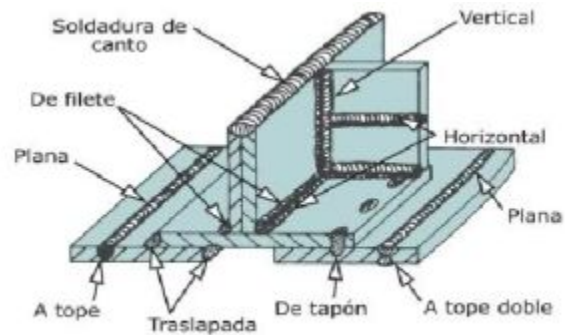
Denominación de los tipos de soldadura
